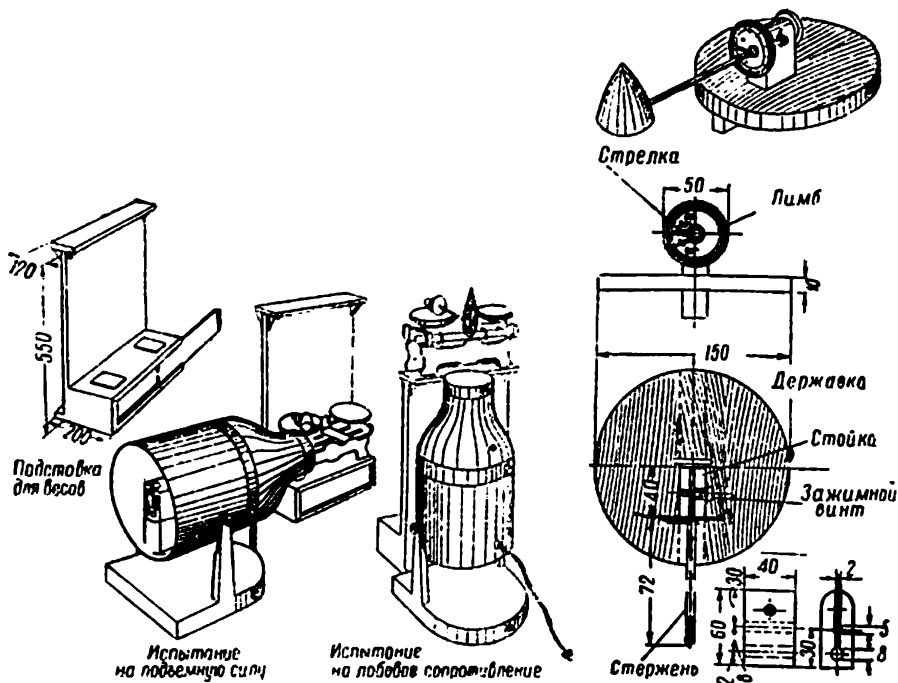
а. Общий вид трубы и деталей приспособления для установки испытываемой модели на весах
